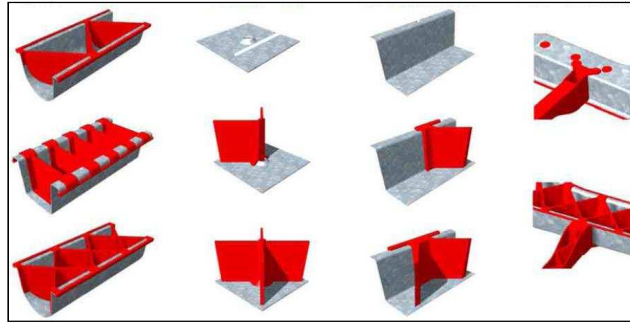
TIPOS DE UNIÓN PARA IN-MOLD ASSEMBLY
